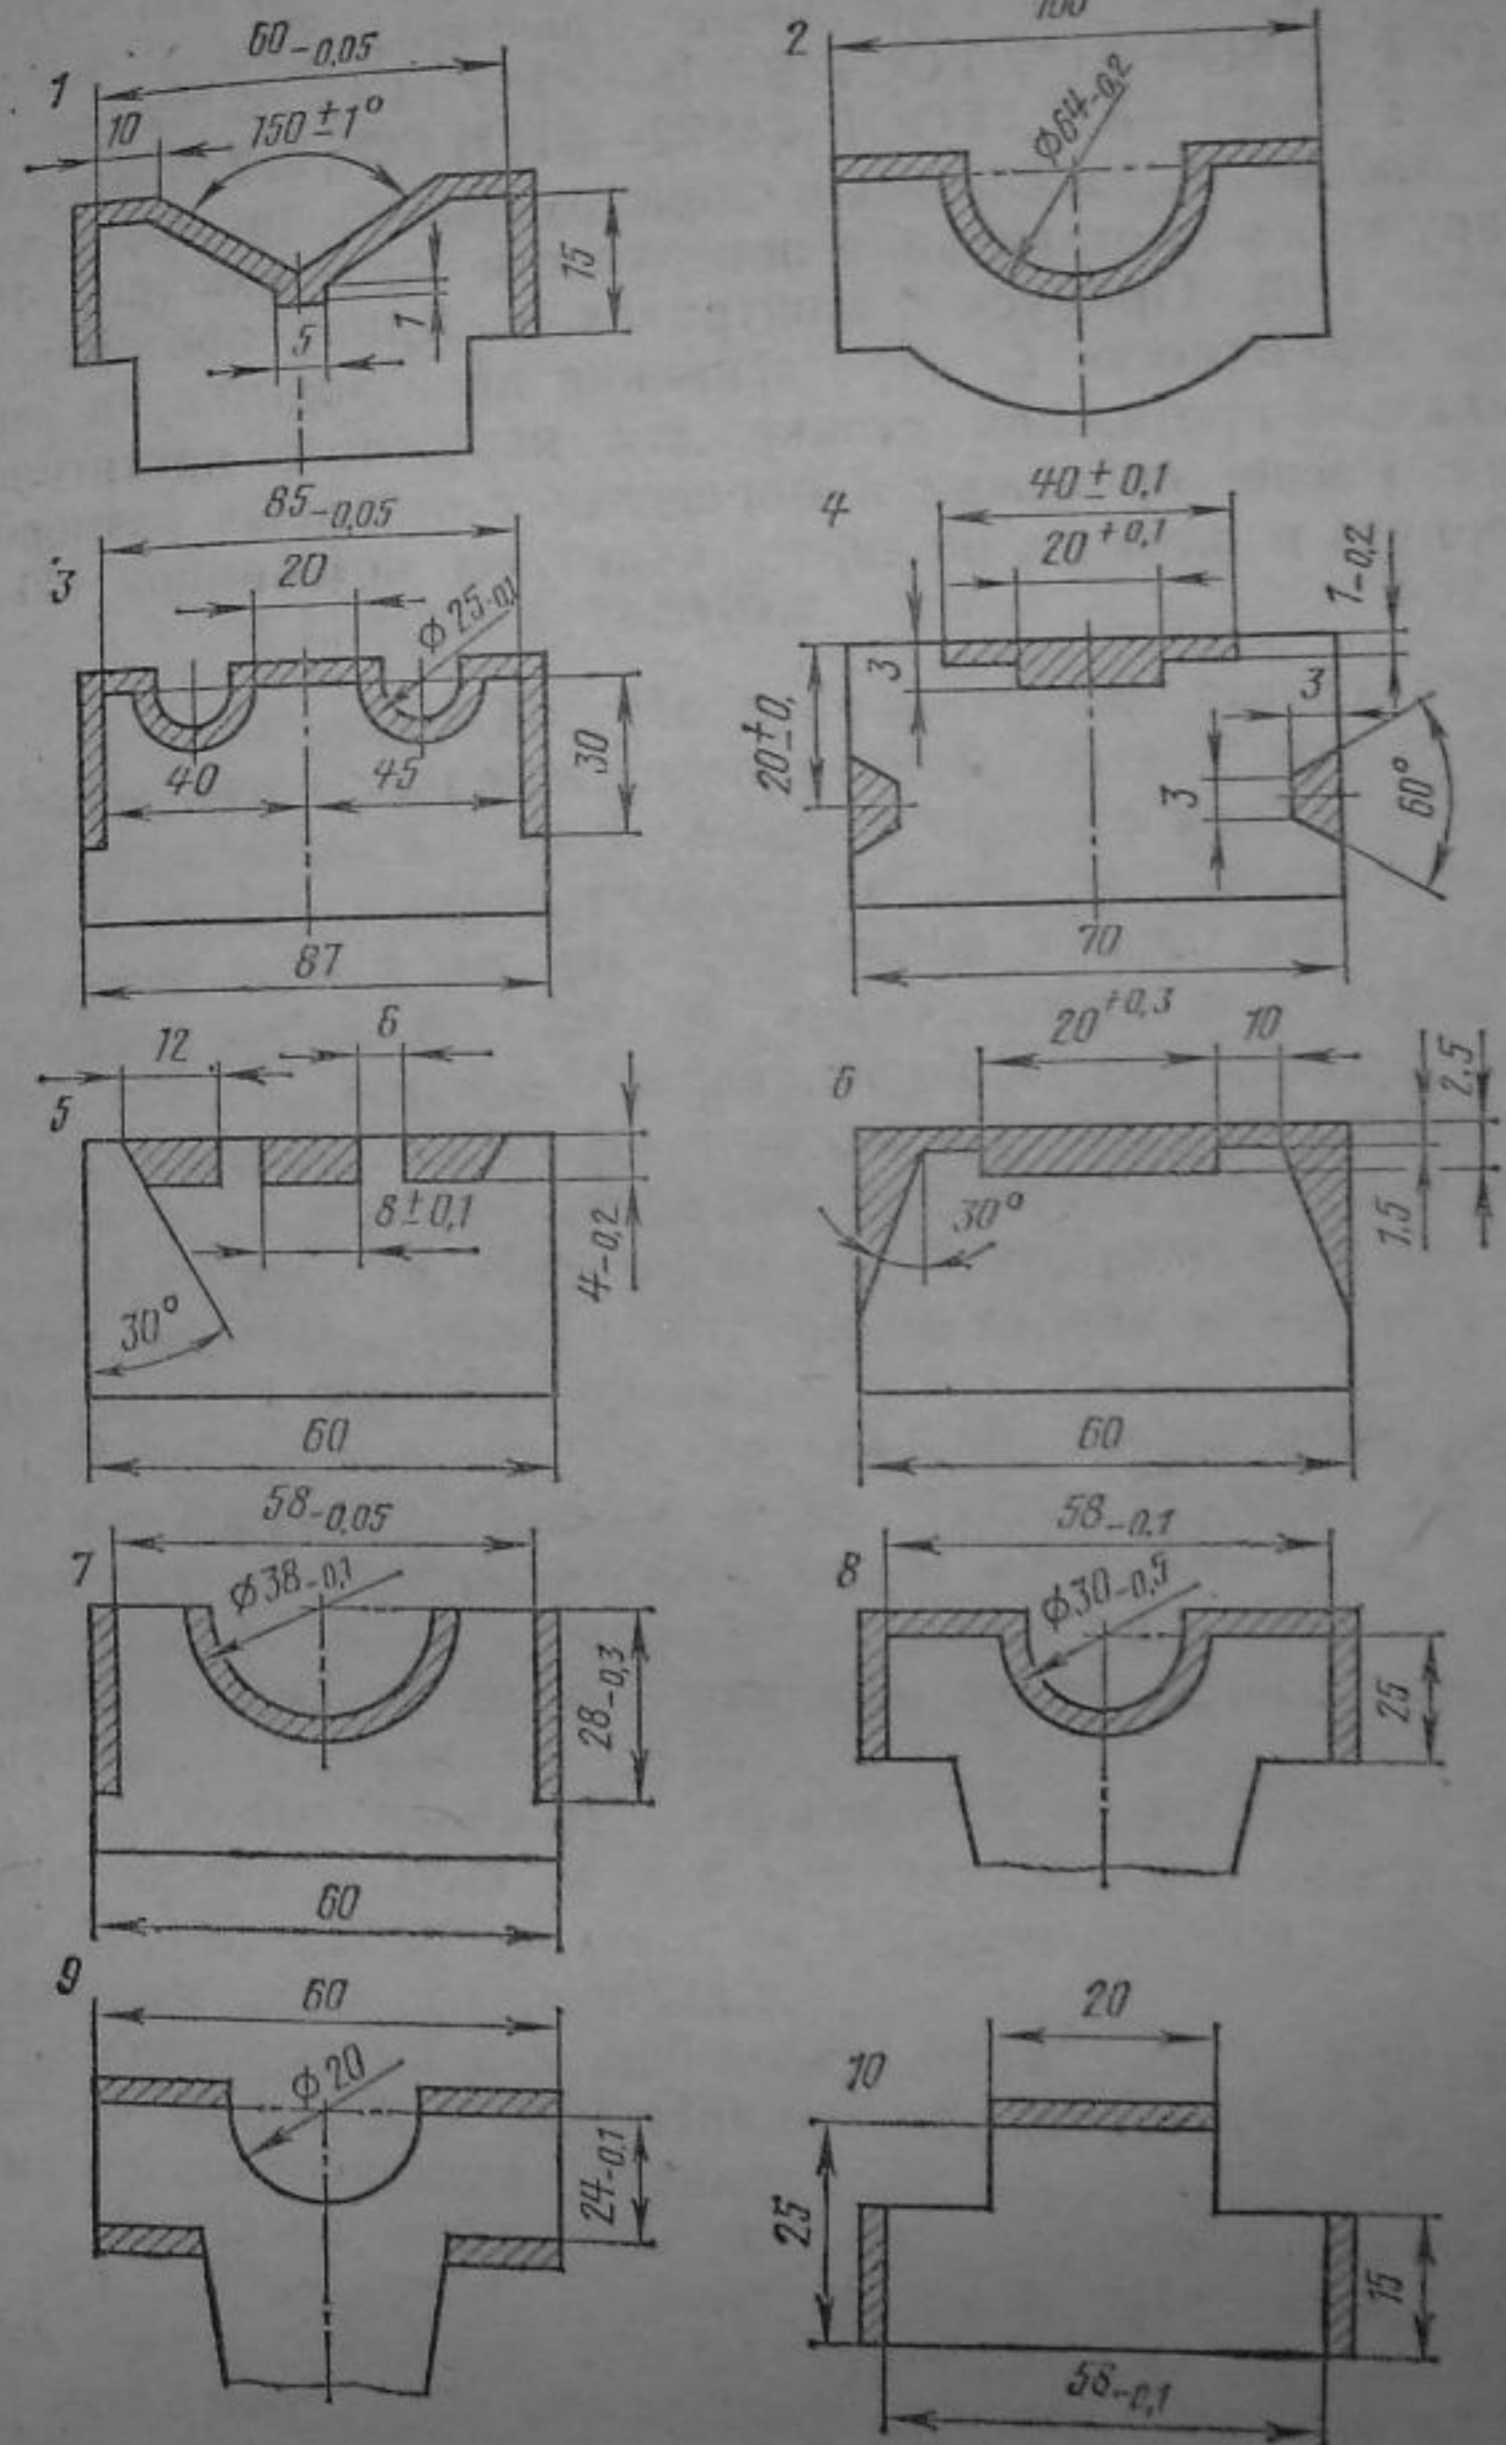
Эскизы обрабатываемых поверхностей заготовок (варианты № 1—10 к задаче 71)
